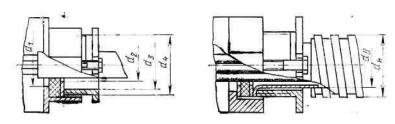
Подключение кабеля с резиновой или пластиковой оболочкой для двигателей с h=200, 225 мм.
